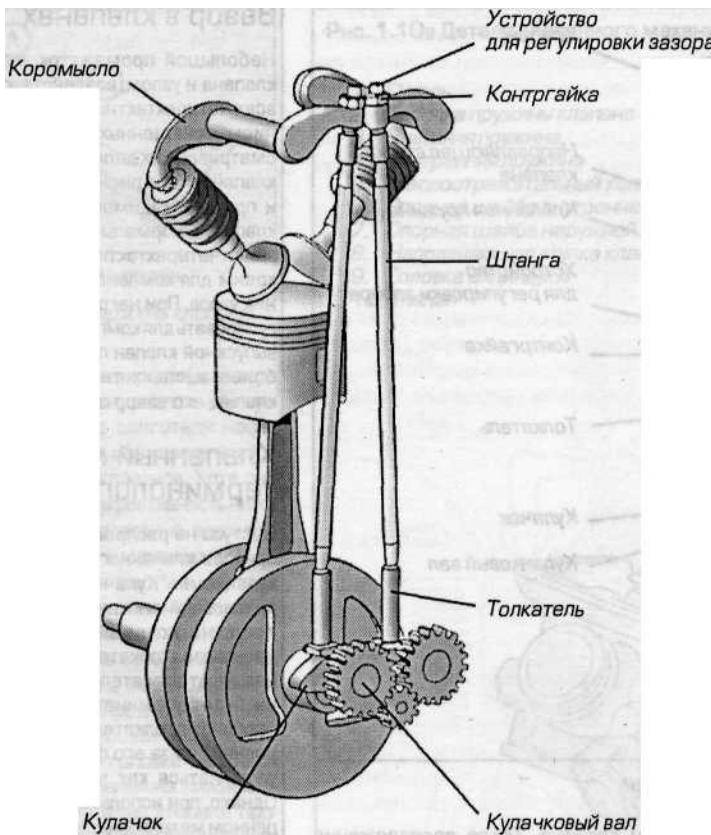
Конструкция верхнеклапанного механизма газораспределения с нижним распределительным валом и штангами
